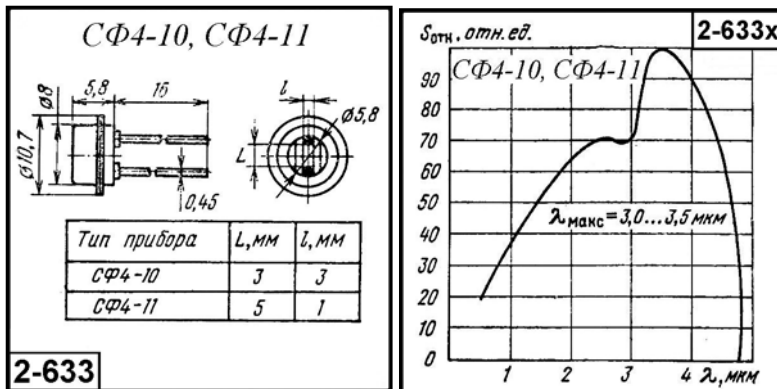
Внешний вид, габаритные размеры и ОСХ ФПУ СФ-4-10 и СФ4-11
